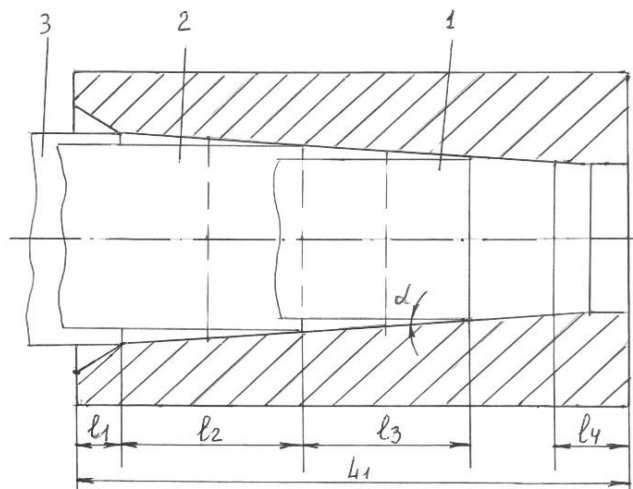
Схема до розрахунку параметрів робочої поверхні матриці для центрування заготовок трьох типорозмірів: 1 — для $\varnothing 130$ мм; 2 — для $\varnothing 150$ мм; 3 — для $\varnothing 170$ мм
